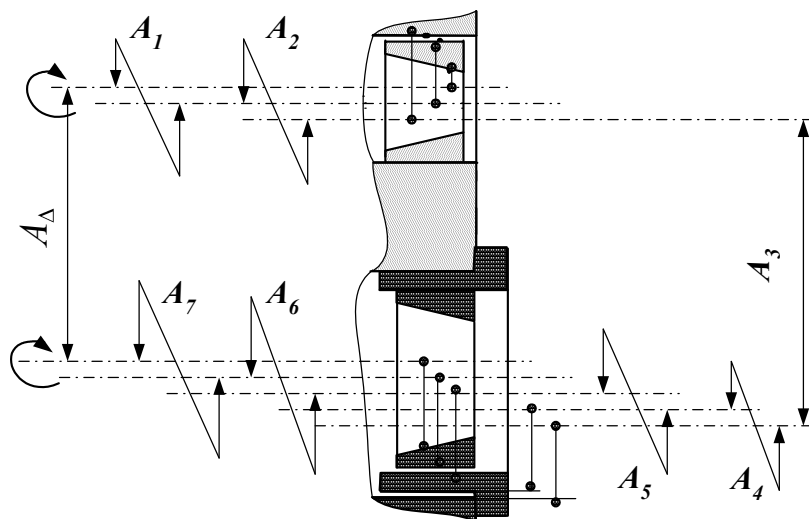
Схема размерной цепи, описывающей формирование межосевого расстояния червячного редуктора
